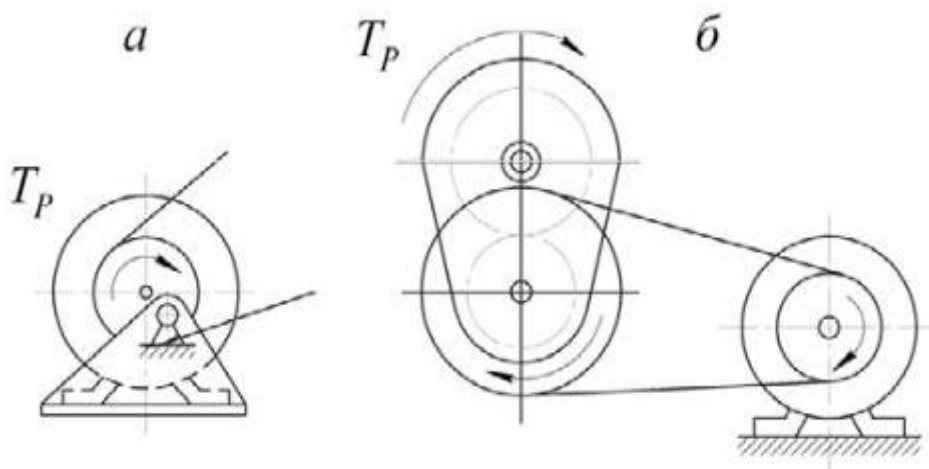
Способы автоматического натяжения ремня за счет реактивного момента: на корпусе электродвигателя (а); на корпусе редуктора (б)
